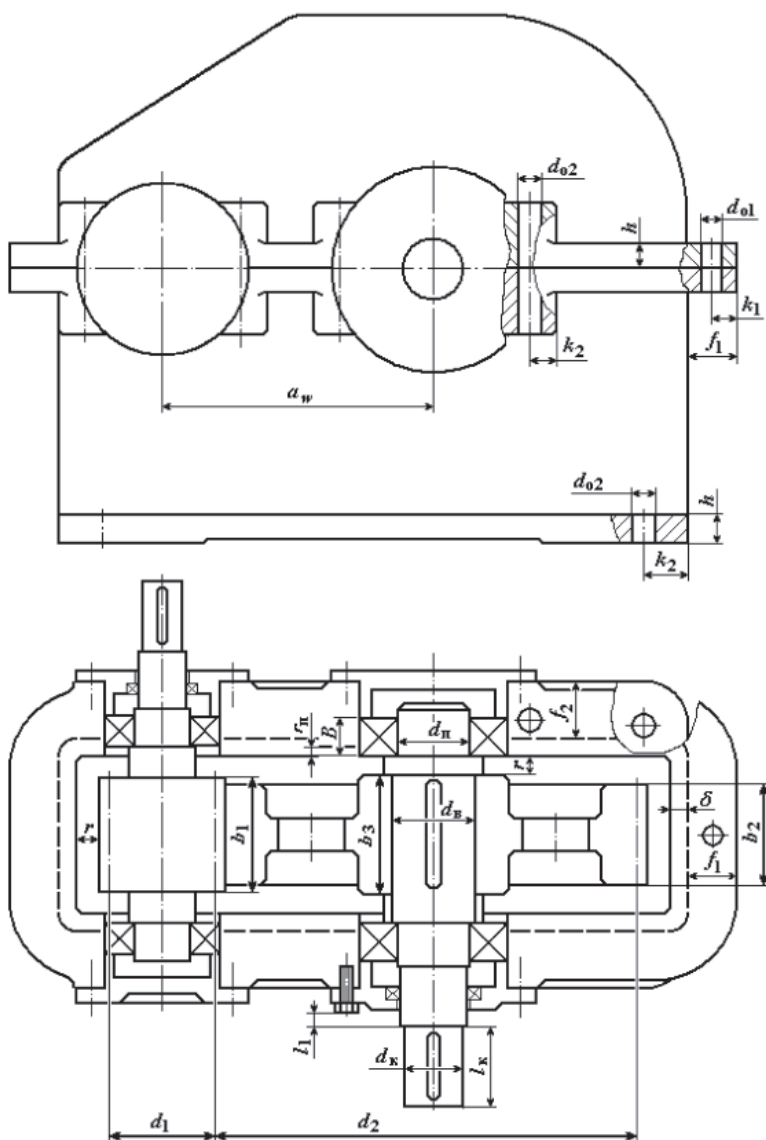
Эскизная компоновка двухступенчатого цилиндрического редуктора
